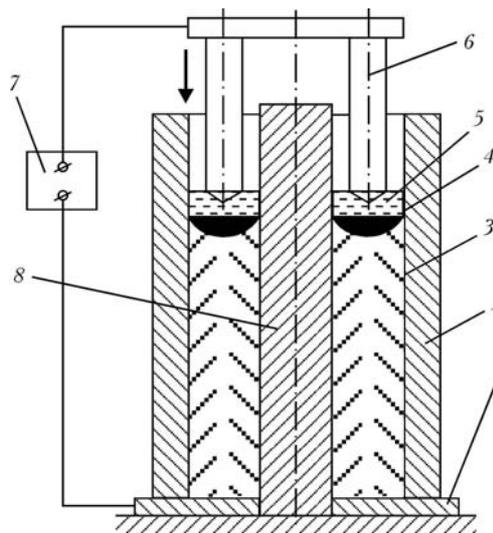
Схема выплавки полых заготовок с неподвижным внутренним кристаллизатором: 1 — поддон; 2 — наружный кристаллизатор; 3 — заготовка; 4 — металлическая ванна; 5 — шлаковая ванна; 6 — расходный электрод; 7 — источник питания; 8 — внутренний кристаллизатор (дорн)
